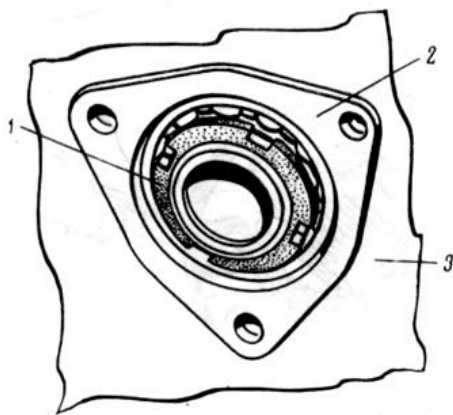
Відкручування гайки кріплення внутрішнього вала: 1- гайка; 2- гніздо підшипника; 3- корпус коробки передач
